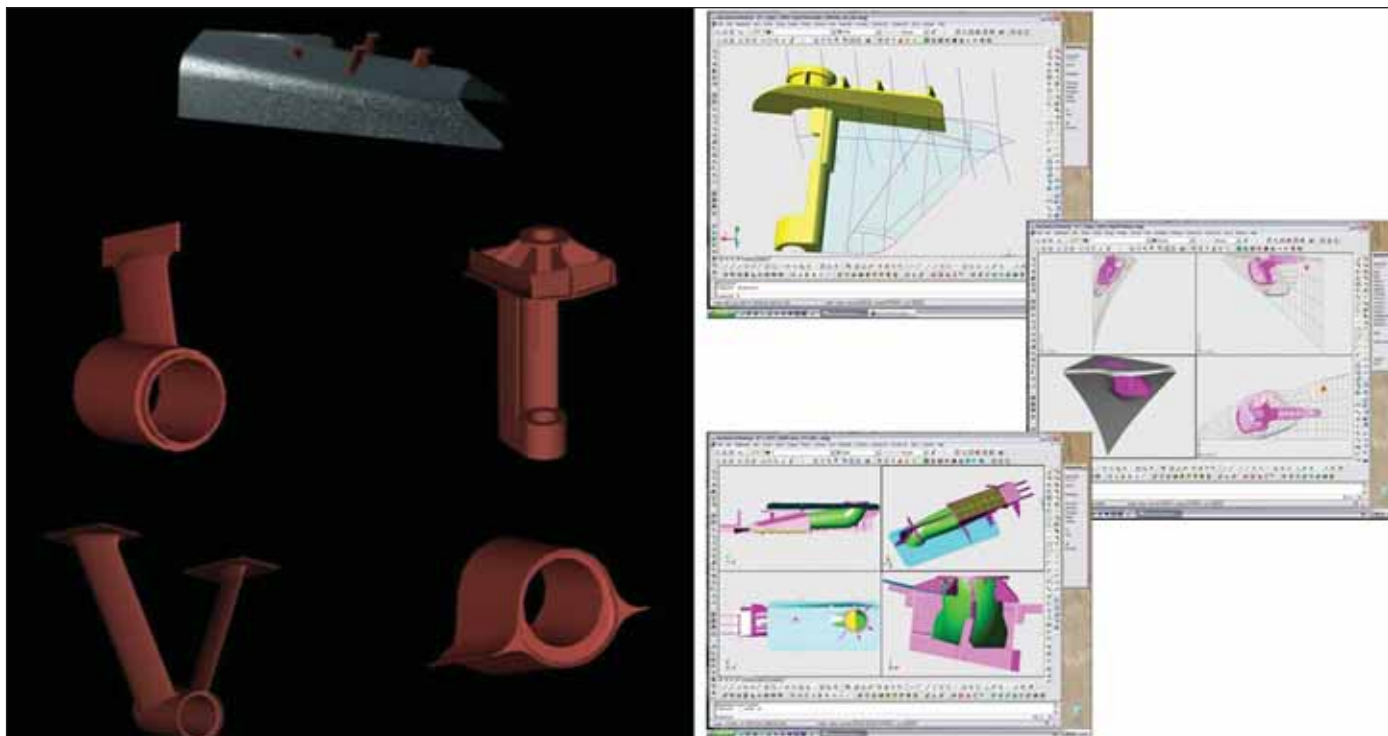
Примеры корпусных конструкций, изготовленных на "Северной верфи"
